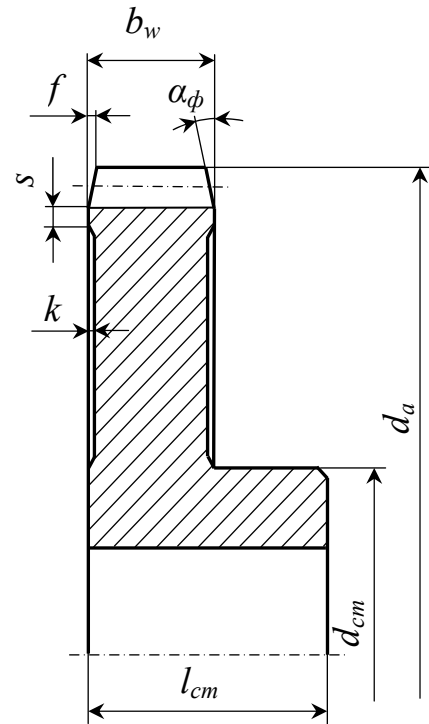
Колесо малого розміру ($d_a \leq 250$ мм)
